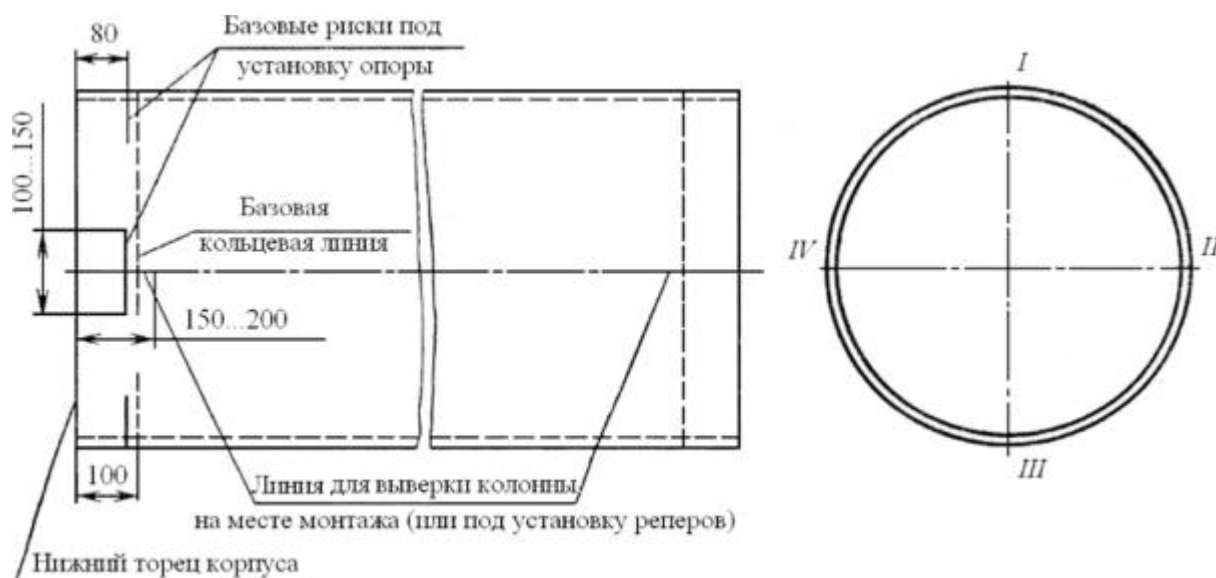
Схема нанесения рисок для установки опоры и выверки колонны на монтажной площадке
